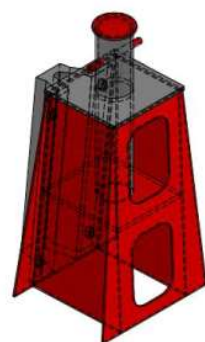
Bollard simple mécano-soudé sur défense réhaussée (AVP)
